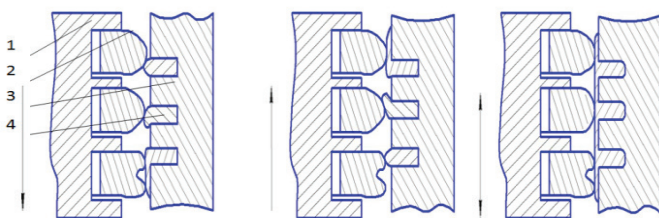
Схема образования плёнки на поверхности гильзы цилиндров: 1-поршень; 2-поршневое кольцо; 3-гильза цилиндров; 4-вставка
